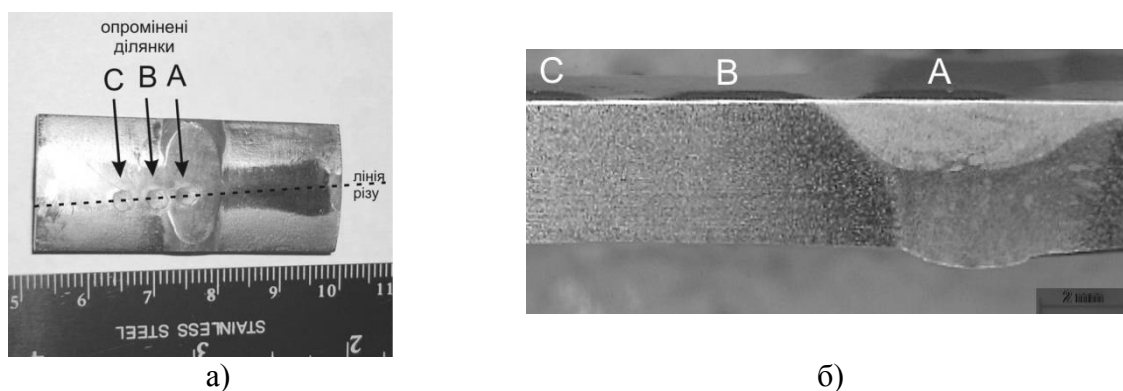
Схема вирізання та опромінення зразка зварного з'єднання: ділянка А над зварним швом, ділянка В та ділянка С над зоною термічного впливу зварювання
